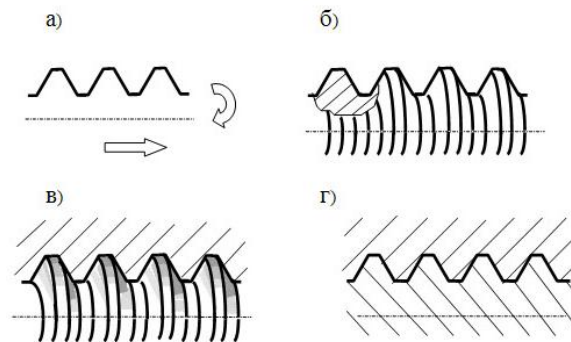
Образование винтовой поверхности цилиндрической резьбы
